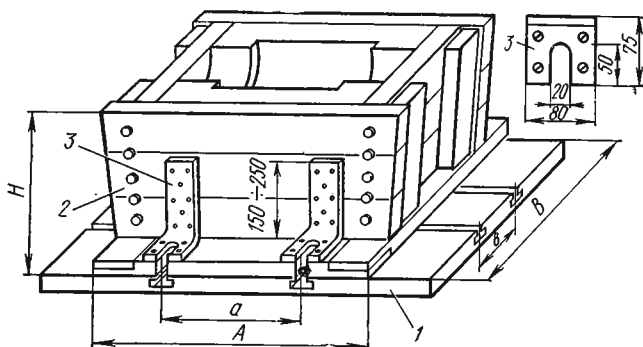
Конструкция стержневого ящика для машинной формовки (размеры см. в табл. 42):
